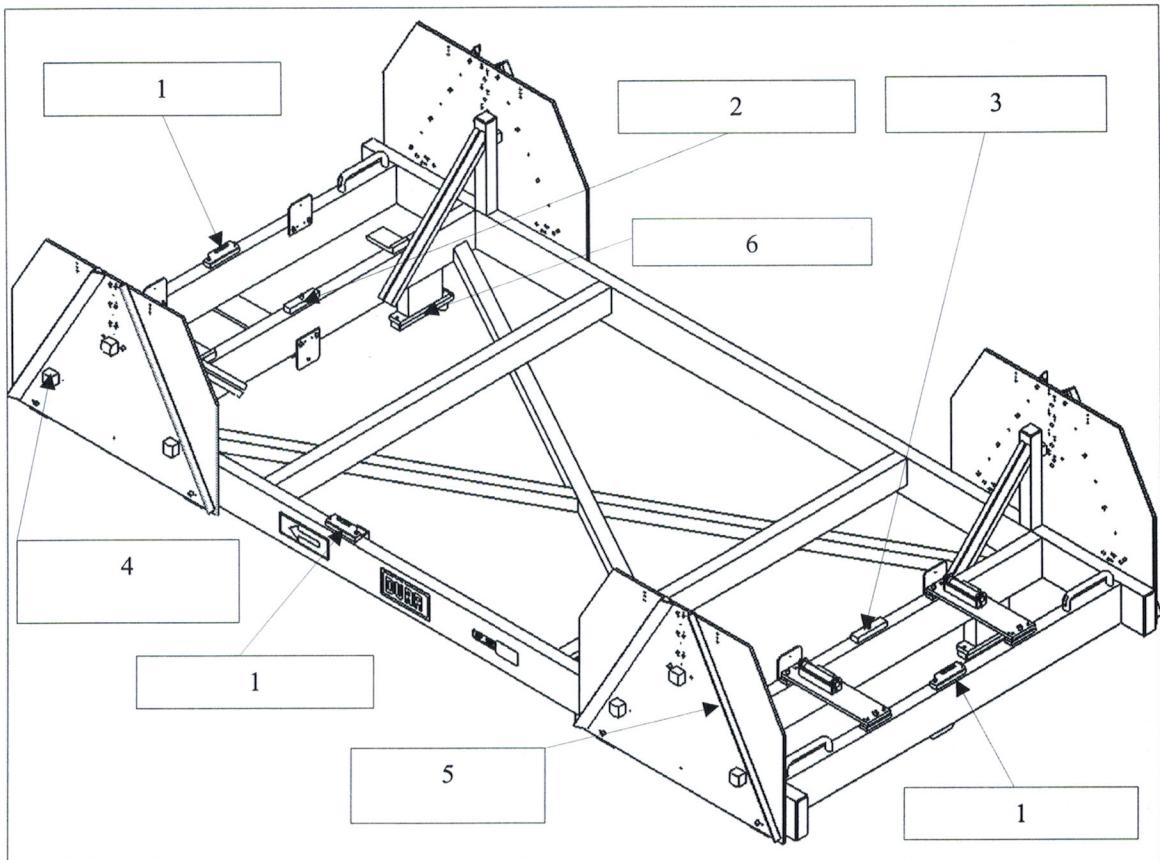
Установка приспособления калибровочного модели Master Gauge на стенде для измерений углов установки колес легковых автомобилей модель x-wheel. 1 – уровни пузырьковые; 2 – центральная точка позиционирования на передней оси; 3 – центральная точка позиционирования на задней оси; 4 – контурные элементы измерительных площадок; 5 – профильные элементы измерительных площадок; 6 – фиксирующие установочные упоры (4 штуки).
